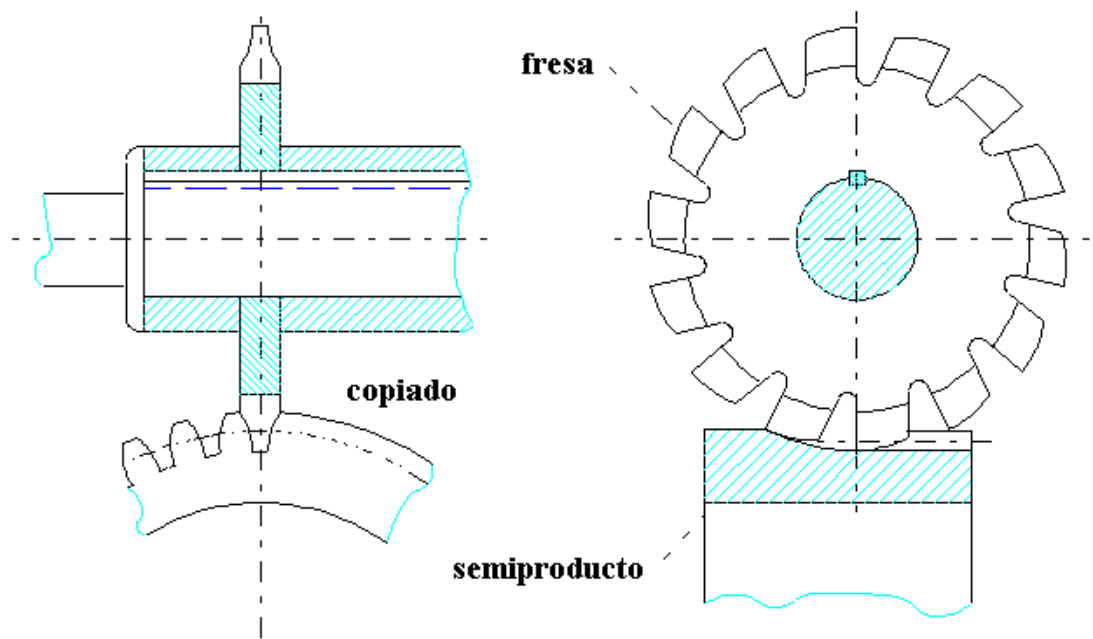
Tallado de engranajes por fresado con fresas de módulo.
